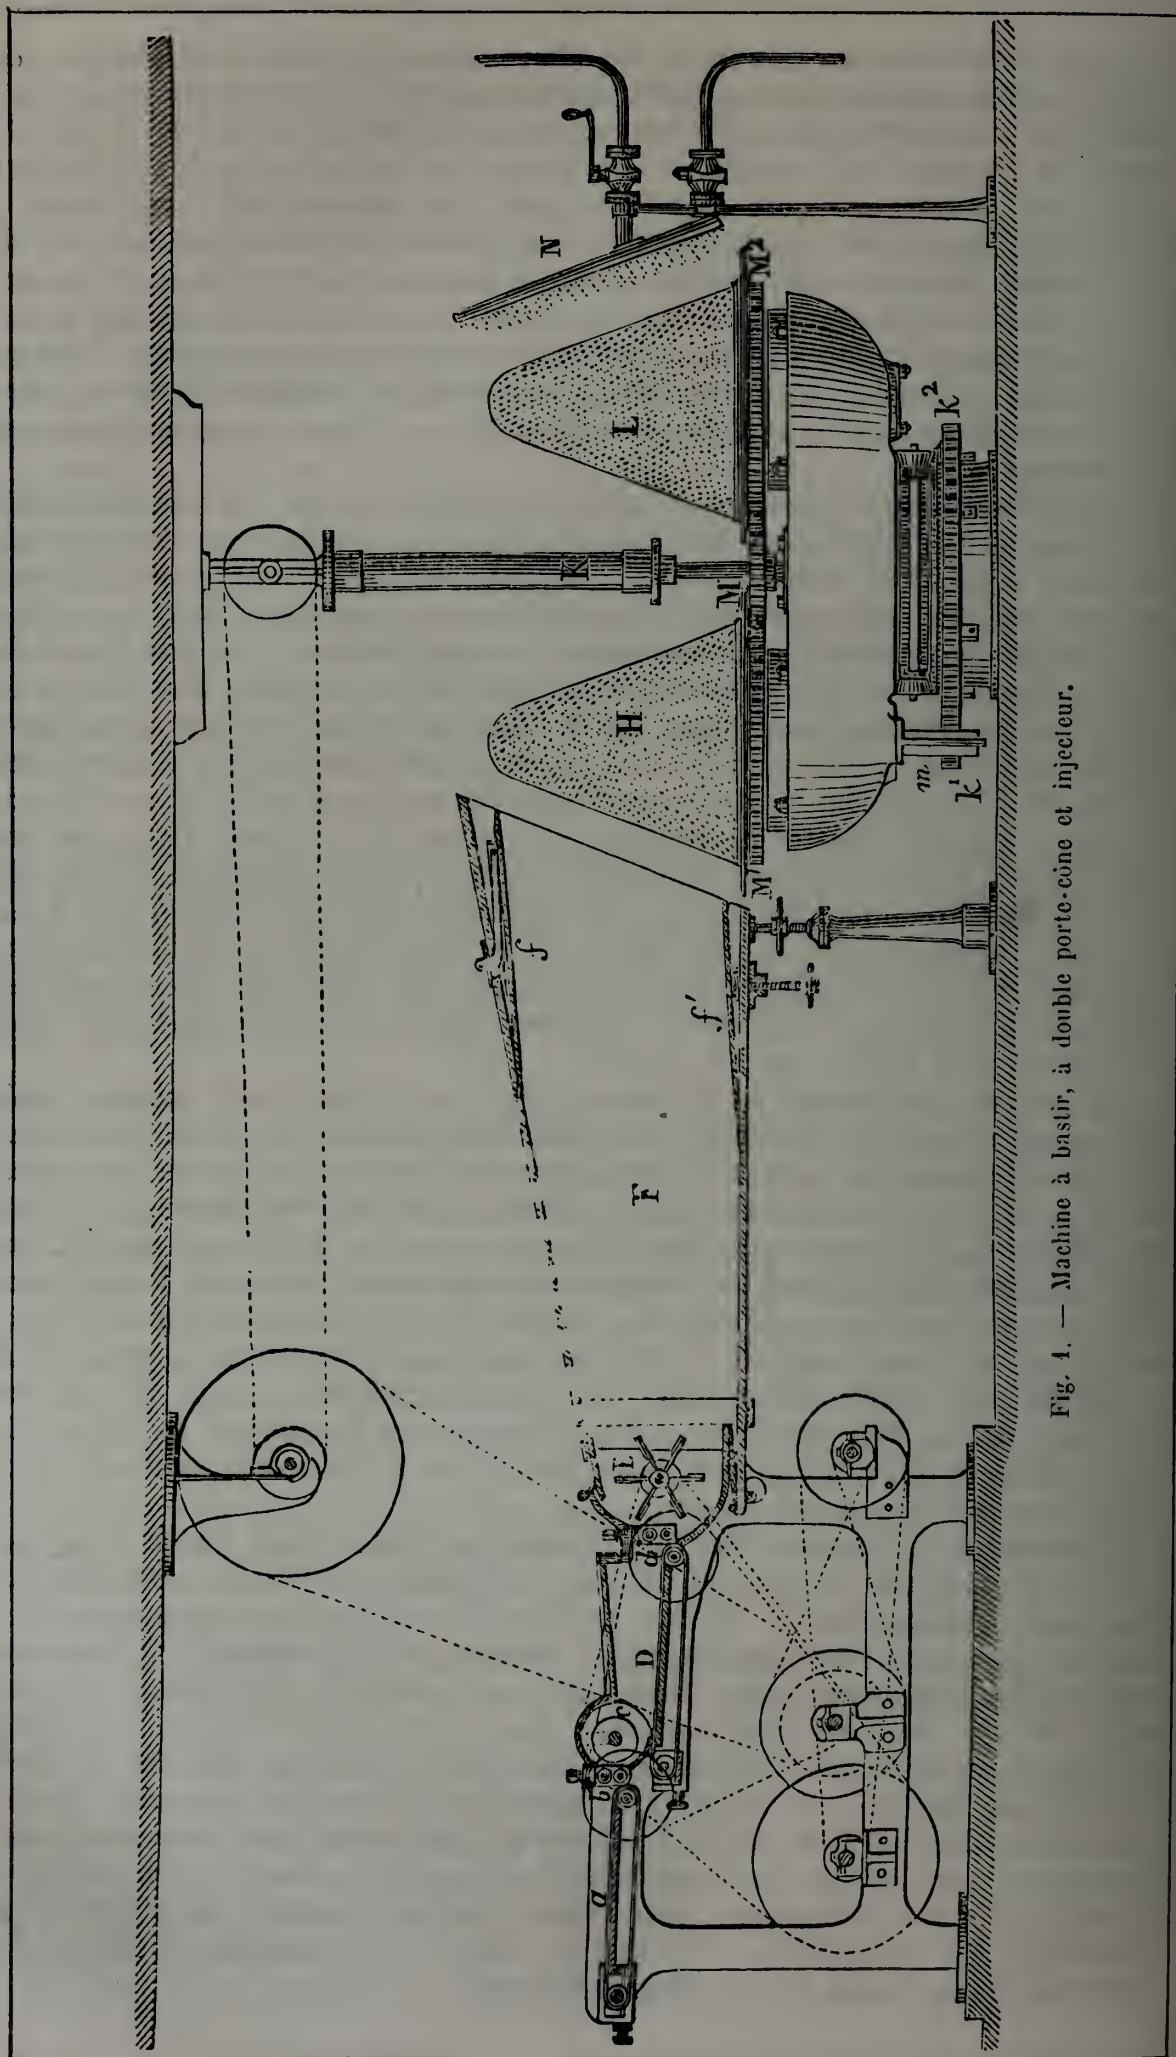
Machine à bastir, à double porto-cône et injecteur.
